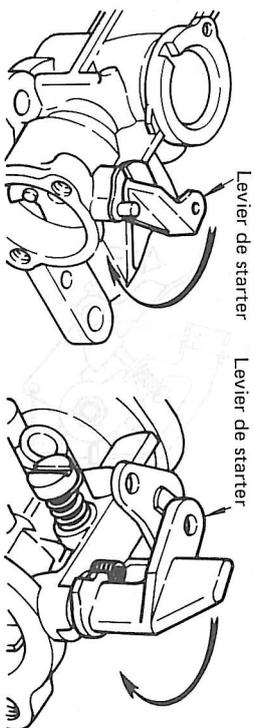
Carburateur type à pompe à impulsion Fig. 5 Carburateur type à flotteur
